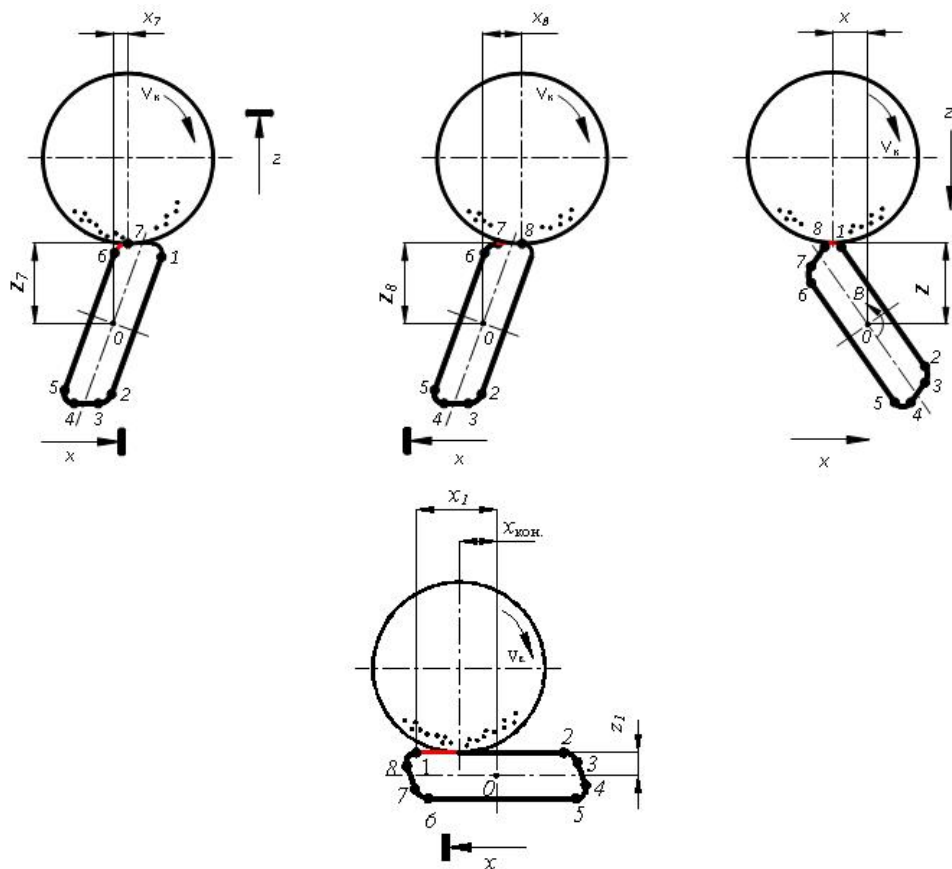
Покадровое перемещение инструмента и заготовки при формировании наружного контура хвостовика (окончание)
